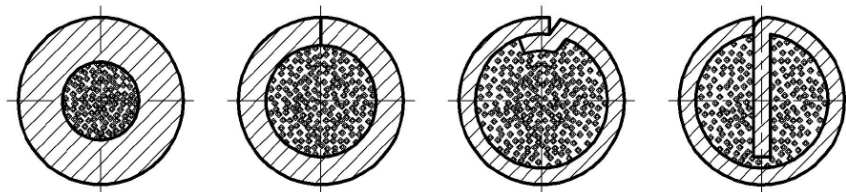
Некоторые конструкции сварочной порошковой проволоки [1]
